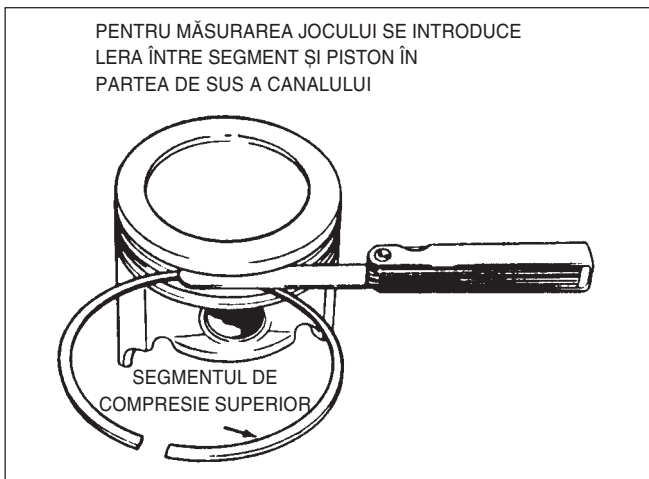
Măsurarea jocului segmentului în canalul de pe piston
